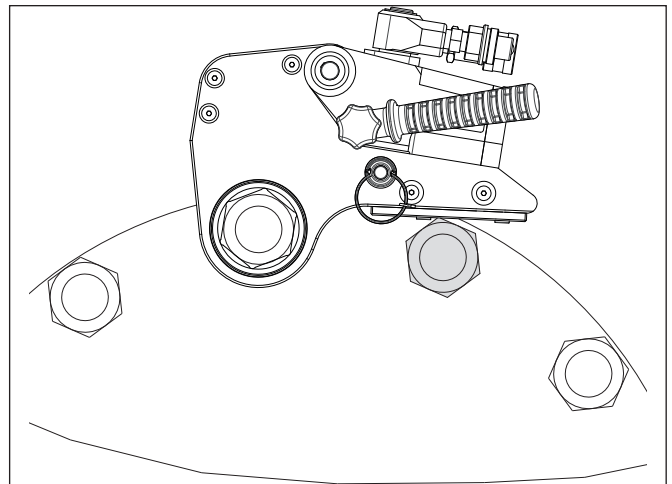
Positionierung des HMT-Werkzeugs mit HLP-Kassette auf einem geeigneten Widerlager
